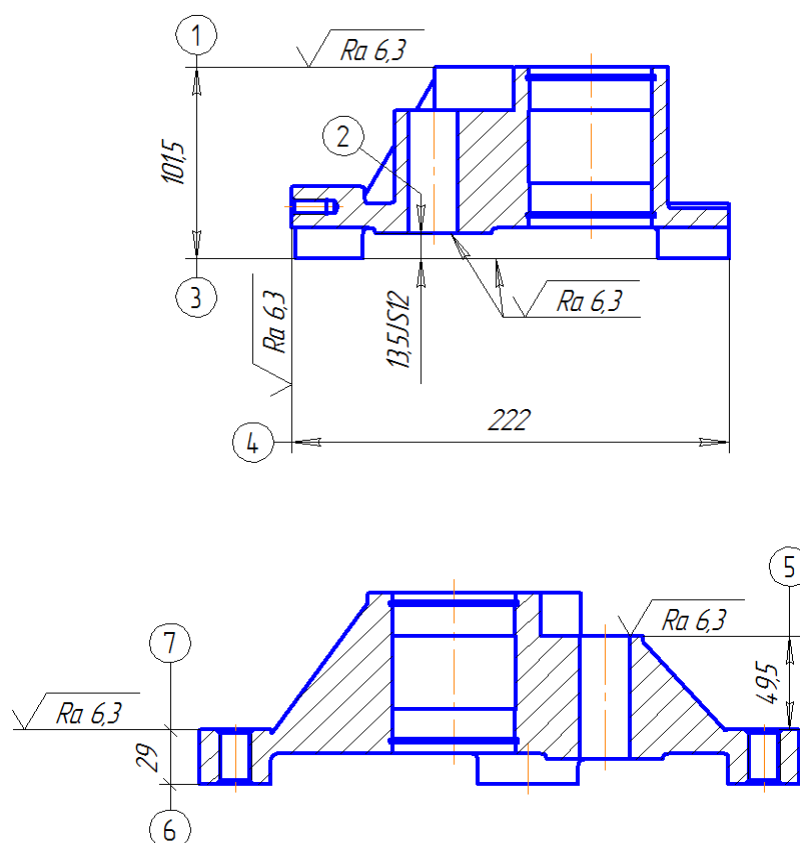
Эскиз детали «Корпус подшипников тягового механизма»
